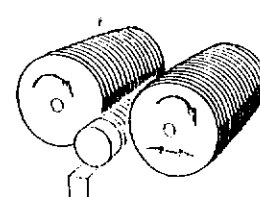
Laminado de roscas con rodillos. a) Pieza; b) rodillos; c) apoyo o guía. La pieza está dispuesta entre un rodillo fijo y uno que se desplaza presionando. Pueden laminarse roscas cortas y largas.
